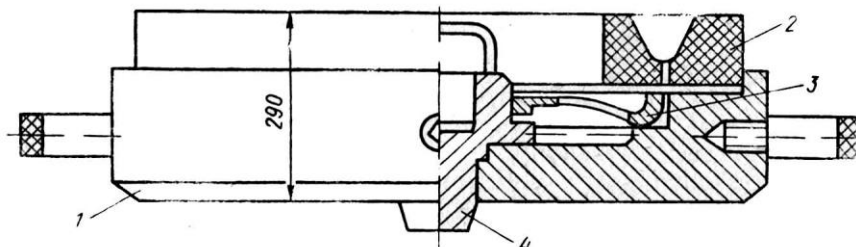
Схема кокіля для відновлення веденого колеса заливанням рідким металом: 1 – кокіль; 2 – ливникова чаша; 3 – колесо; 4 – центрувальна вісь
